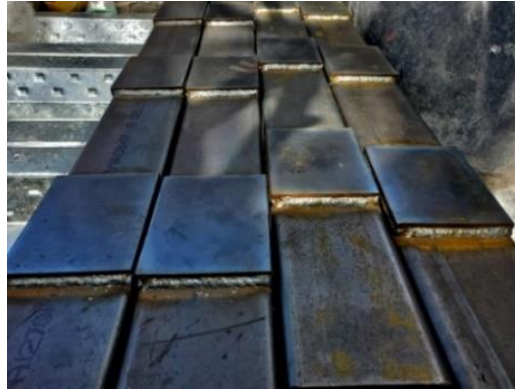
Platinas unidas mediante soldadura a la viga
